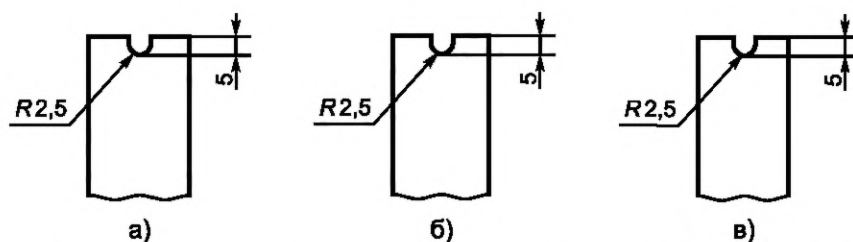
Примеры конструкции вершины стойки оборудования для бадминтона классов A и B
